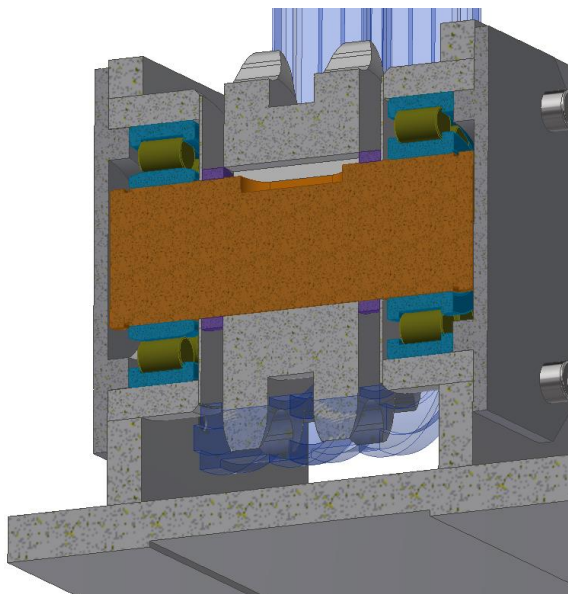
Původní dvojice ložisek podstavy řetězového kola [34]
